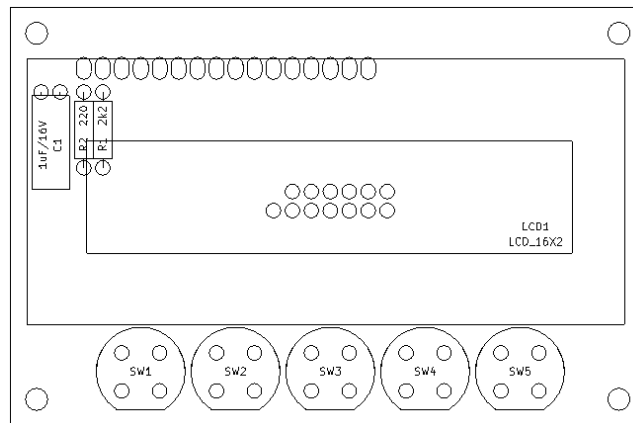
Layout do PCB da Interface Pessoa-Máquina
